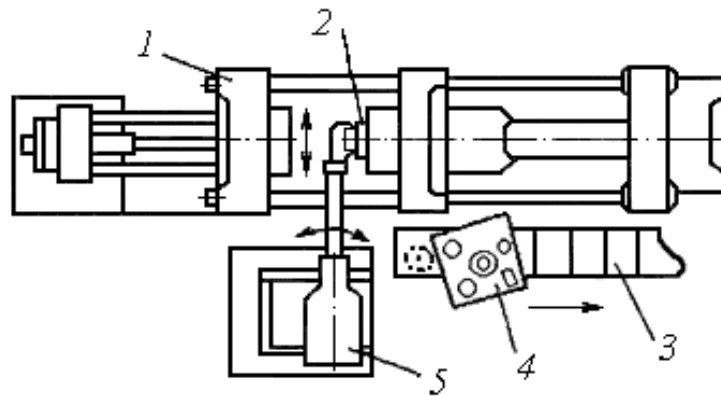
Схема РТК для производства заготовок методом литья под давлением:
